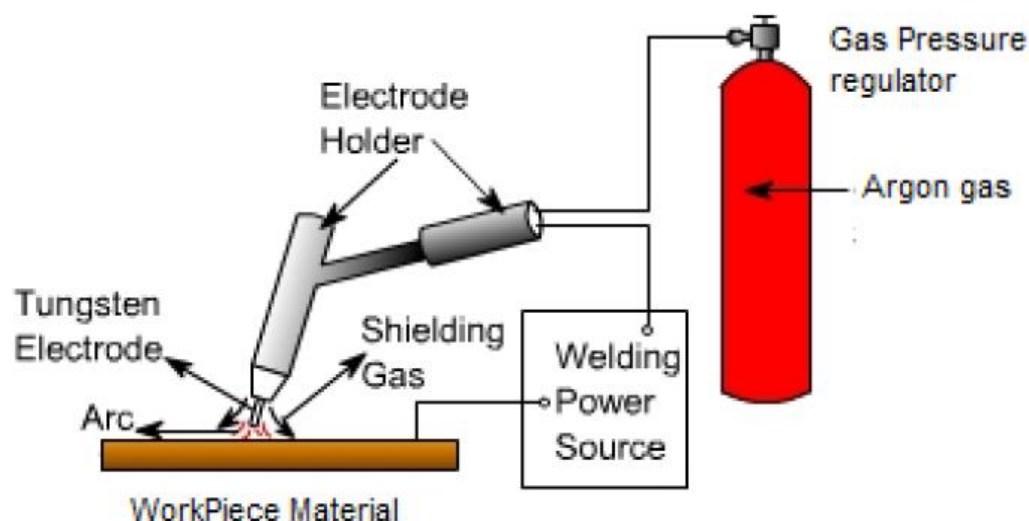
Illustration schématique du procédé de soudage TIG [25].
